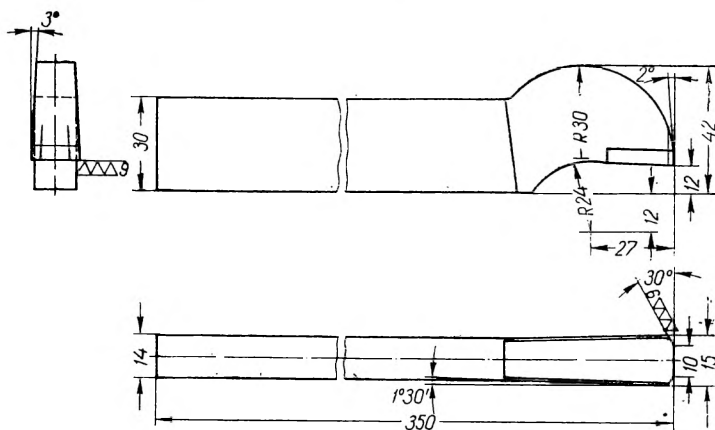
Приспособление для расточки отверстий под пальцы в соединительных муфтах.
